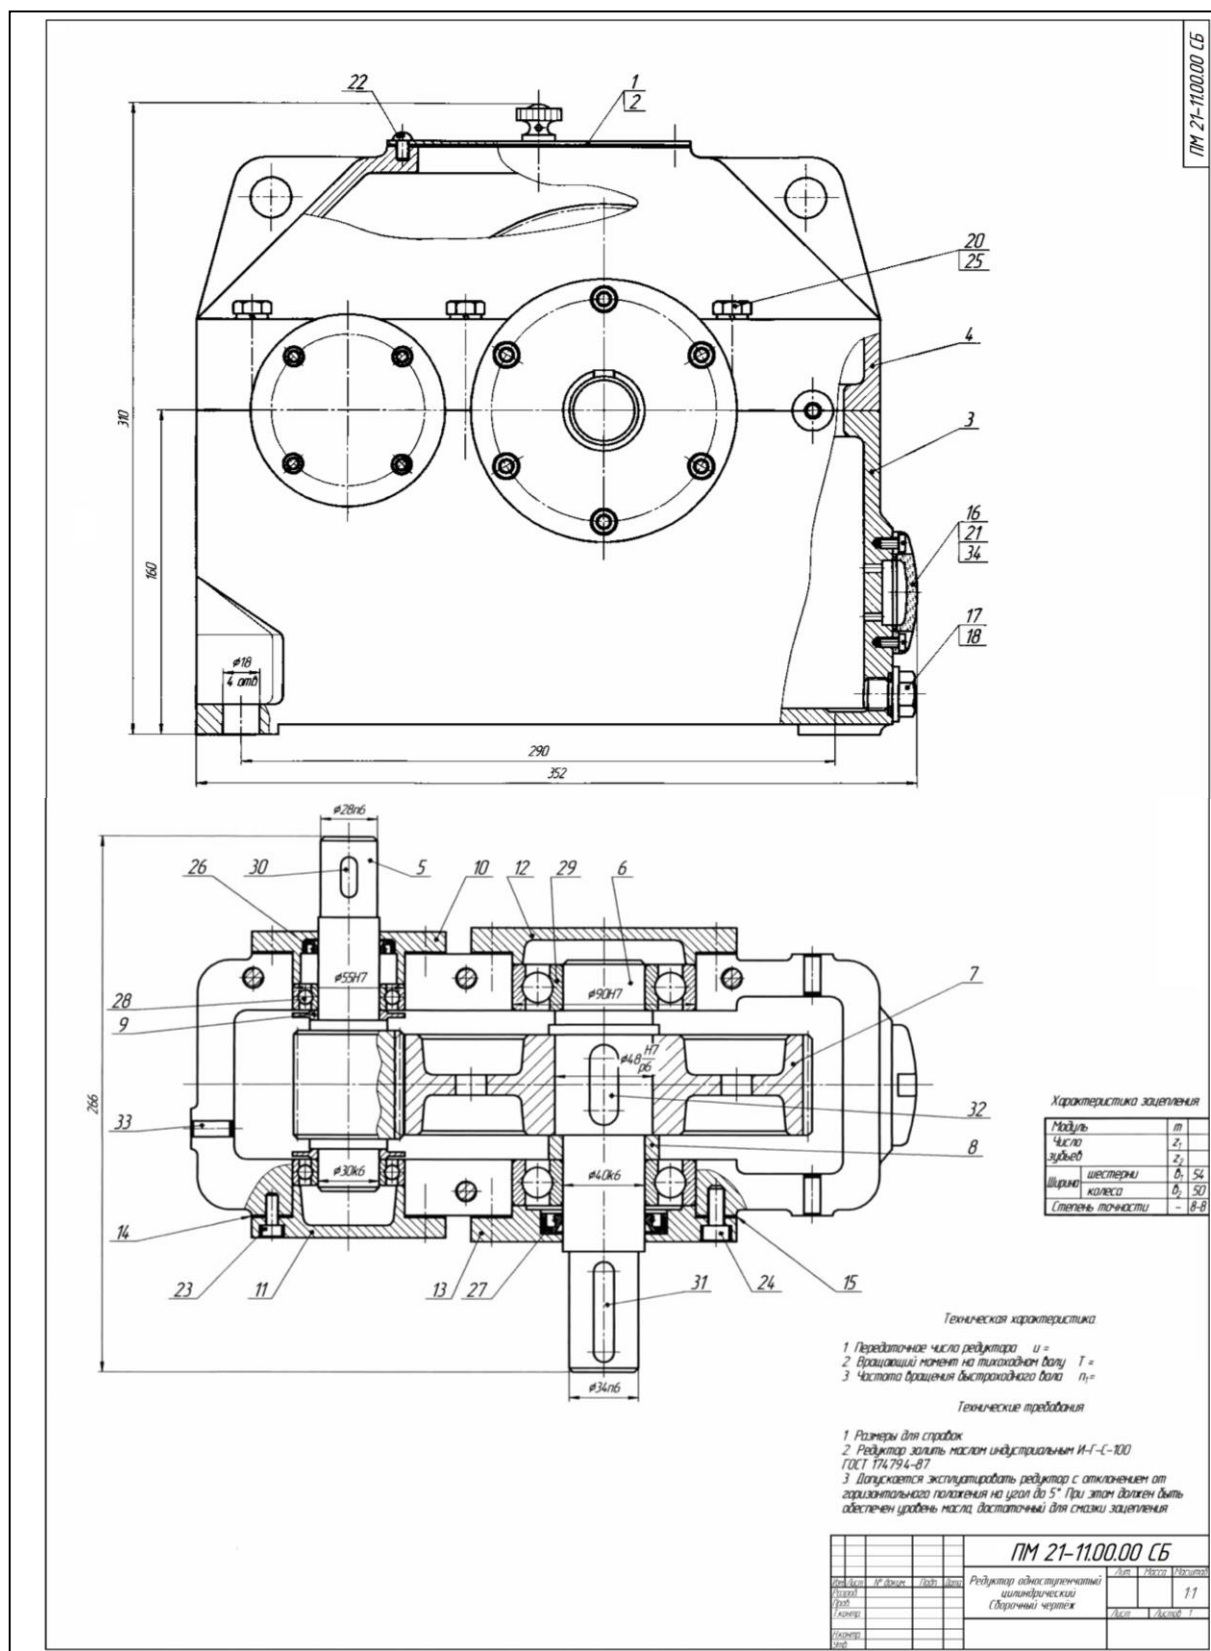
Пример сборочного чертежа одноступенчатого цилиндрического редуктора
